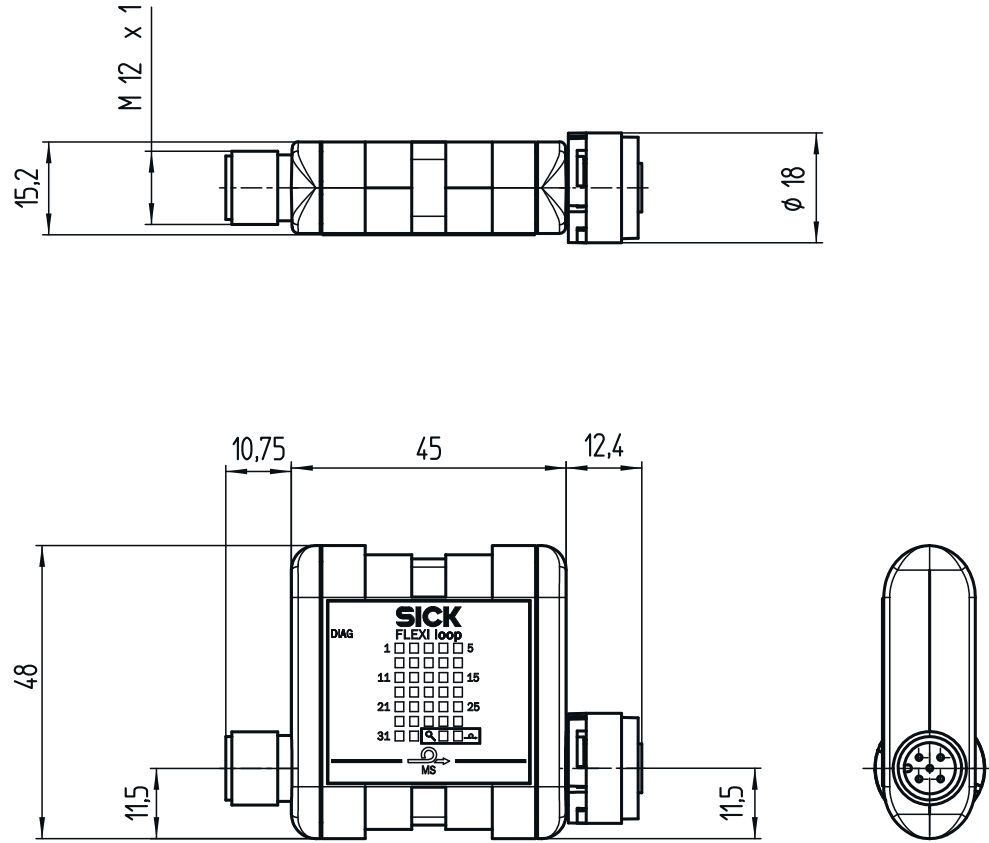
Plan coté des accessoires Flexi Loop DIAG (mm)
